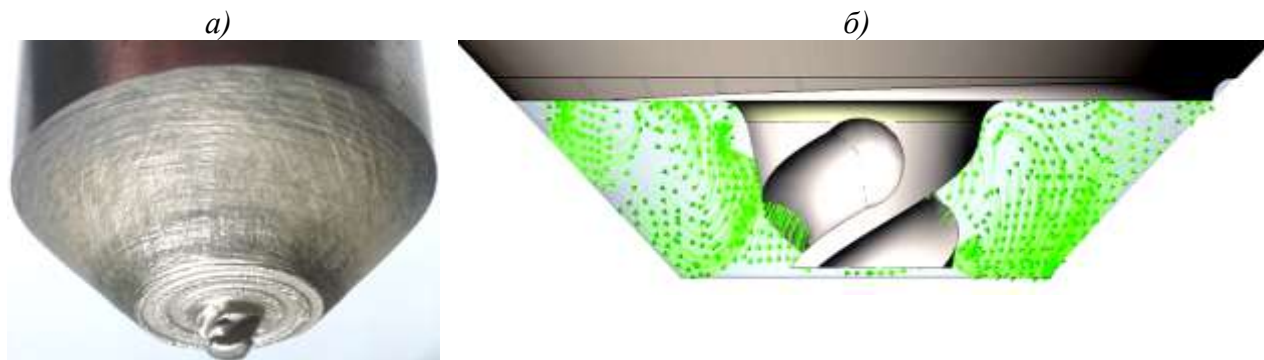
Сложнопрофильный инструмент для сварки трением с перемешиванием листового материала (а) и моделирование воздействия инструмента на свариваемый материал (б) [13]
